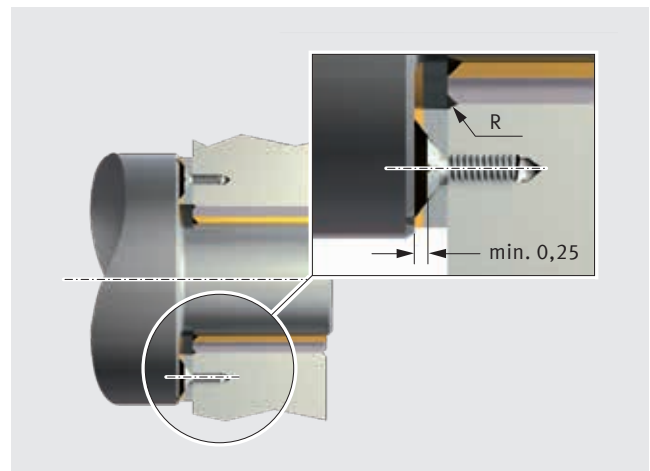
Befestigen einer Anlaufscheibe PAW ohne Ausnehmung im Gehäuse
